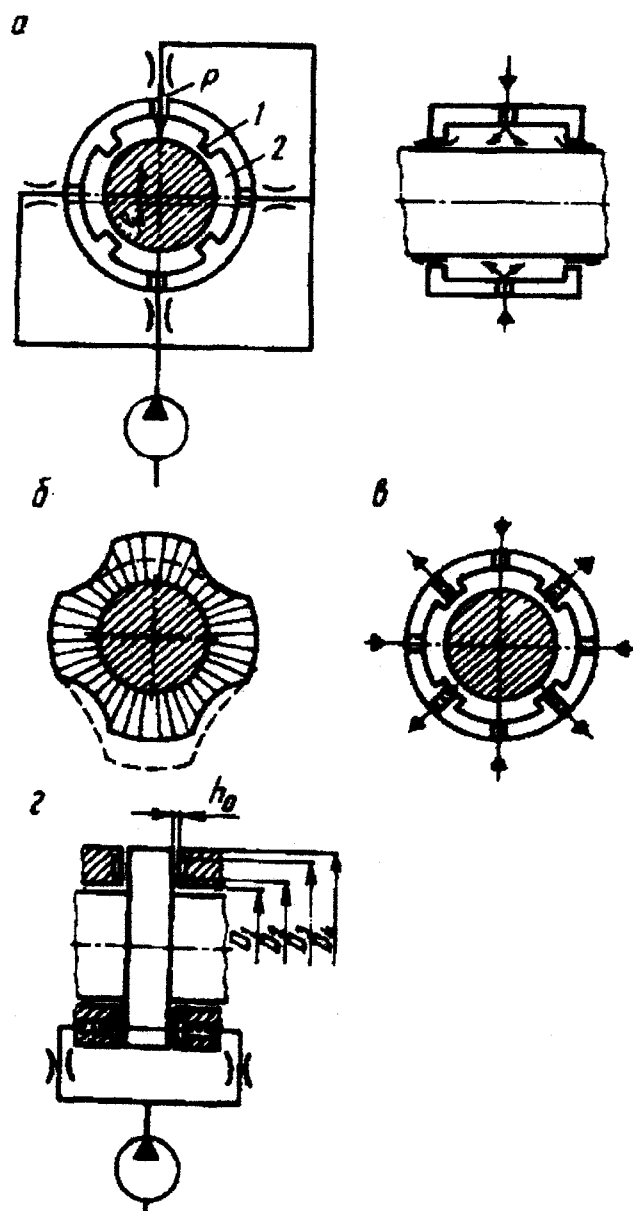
10. Схемы гидростатических подшипников: а) радиальный подшипник: 1 - перемычка, 2 - карманы; б) эпюра давлений; в) гидростатический подшипник; г) гидростатический упорный подшипник
